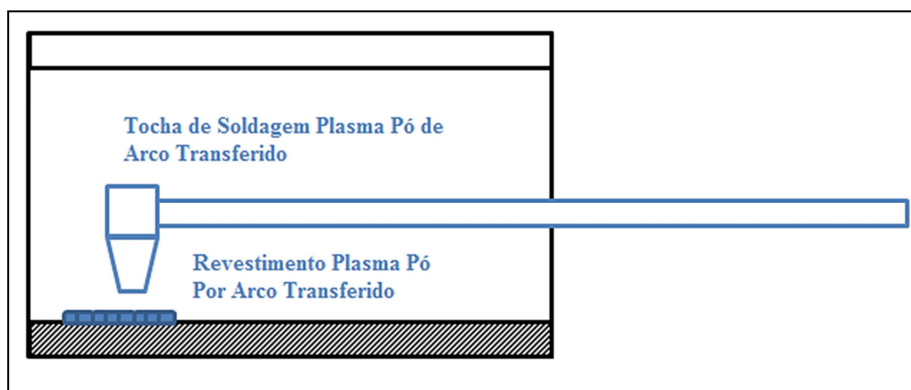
Revestimento ou cladeamento interno do tubo de aço carbono pelo processo de soldagem de revestimento plasma pó, PTA.
